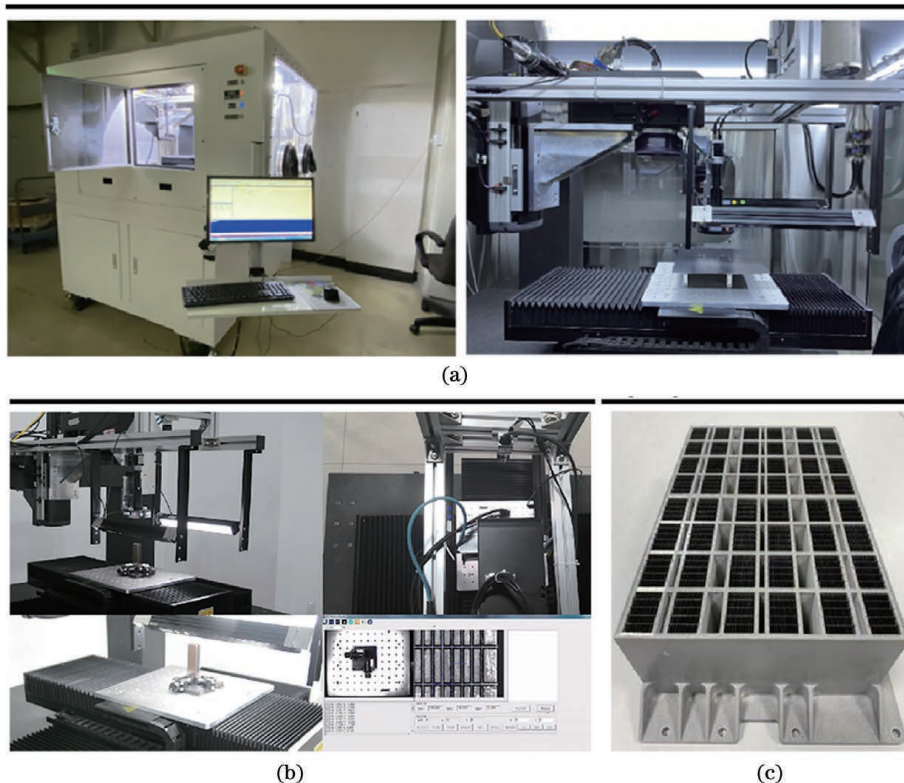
装备整机及准直器实物。(a) 装备实物; (b) 焊接过程; (c) 准直器部件
